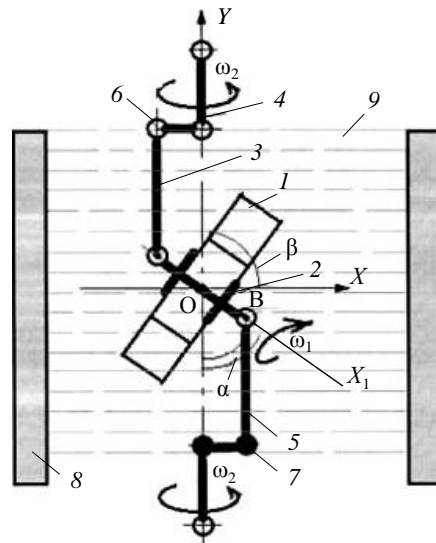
Схема оснастки с вращением детали в разных плоскостях [28]: 1 – деталь; 2 – вращающаяся ось крепления детали; 3 – верхний шток крепления механизма наклона детали; 4 – вращающийся шток привода; 5 – нижний шток крепления механизма наклона детали; 6, 7 – верхний и нижний поворотный кулачок привода; 8 – катодный испаритель; 9 – поток плазмы
